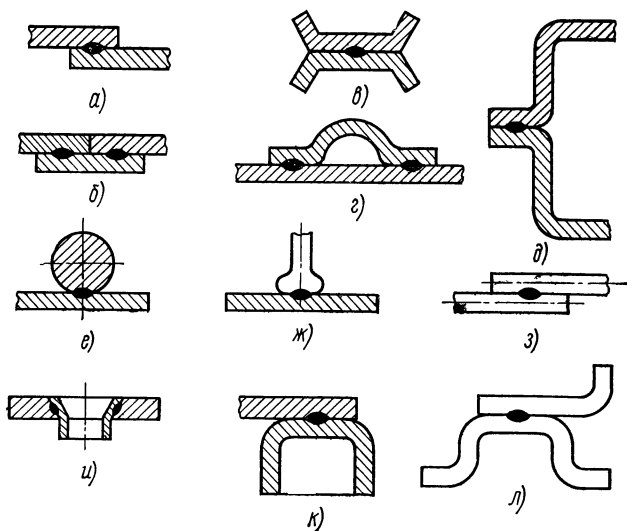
Соединения, выполненные ультразвуковой сваркой
